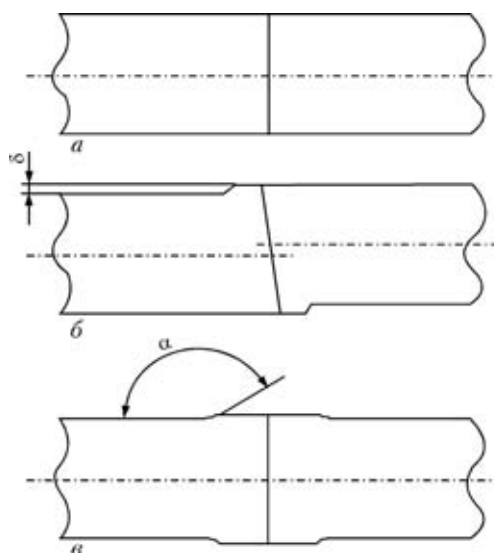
Схемы сварных соединений, полученных КСС, со снятым гратом (а), смещением δ свариваемых кромок (б) и усилением (в)
